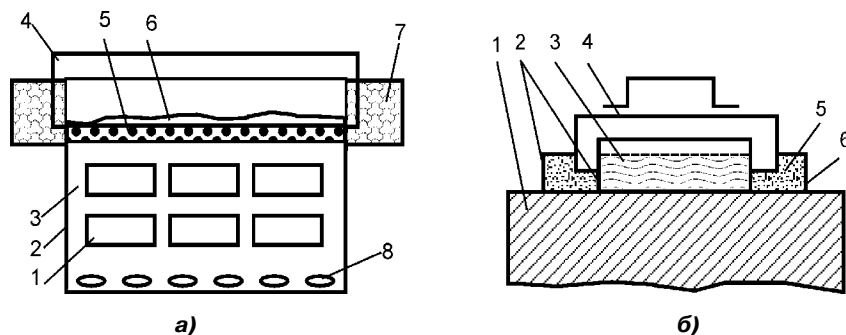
Схема упаковки деталей при общем или местном борировании в порошке:
